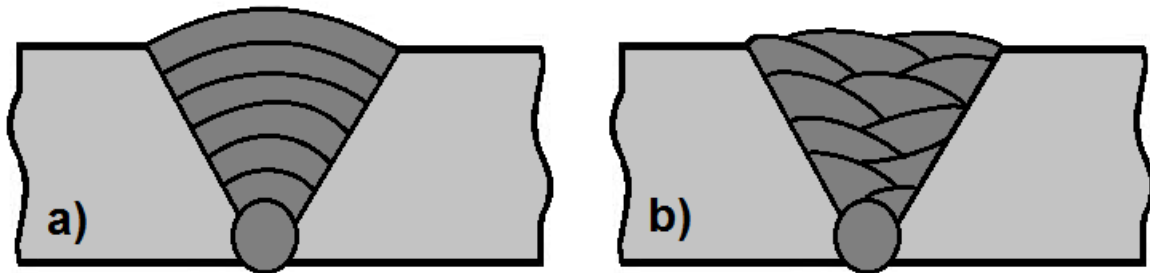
Técnicas de soldadura de cordones (a) anchos y (b) angostos (18, 74)
